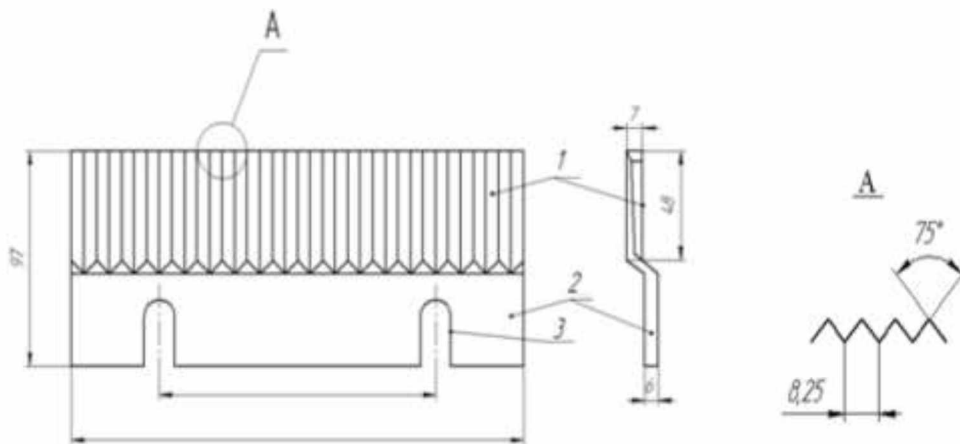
Конструкція ножа відцентрової бурякорізки: 1 – ріжуча площа; 2 – робоча частина ромбовидної форми; 3 – привалочна установча площа
